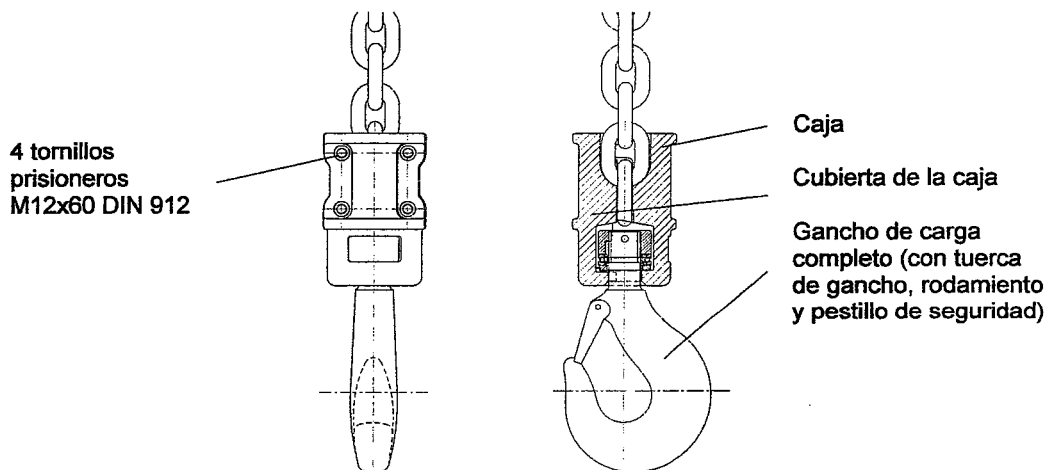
Estructura de la caja del gancho de cadena diámetro 16x45 mm
